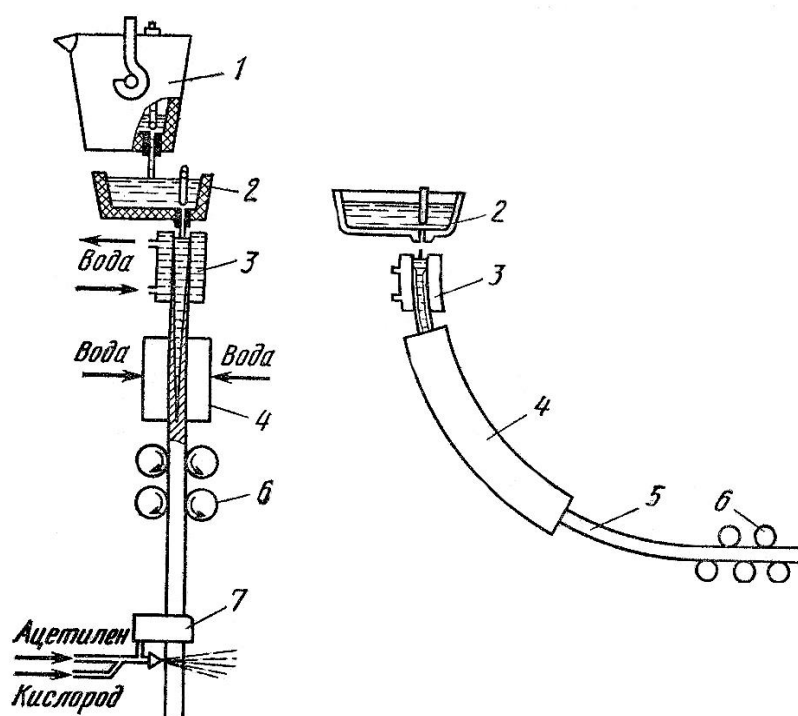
Схемы установок непрерывной разливки стали:
